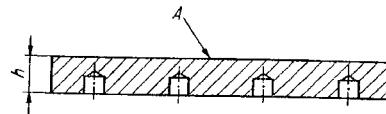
Планка 3, 4 уплотнительная /рис. 111/
